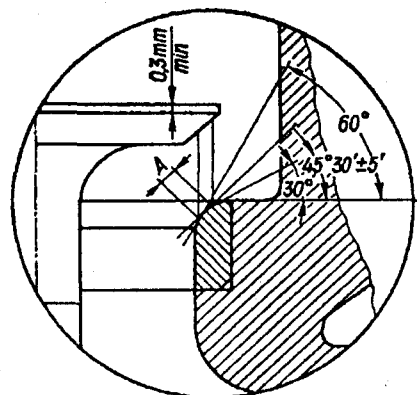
Углы шлифовки седла клапана: А – ширина фасок седел для впускных клапанов 0,43...1,43; для выпускных клапанов 1,57...2,57 мм
